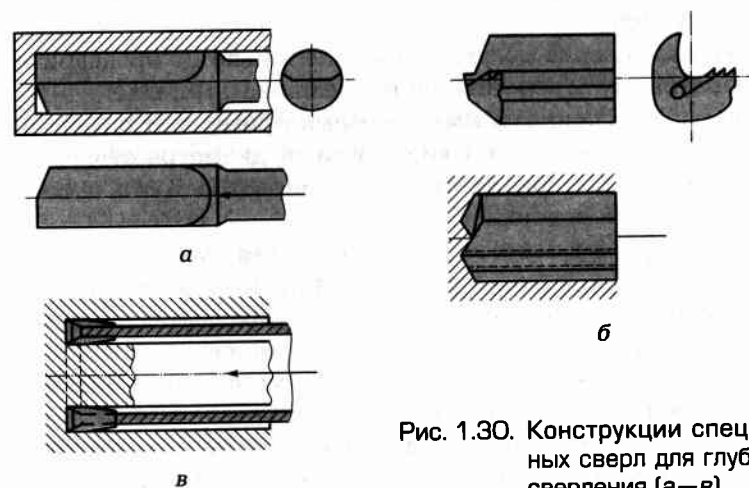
Конструкции специальных сверл для глубокого сверления (а—в)
